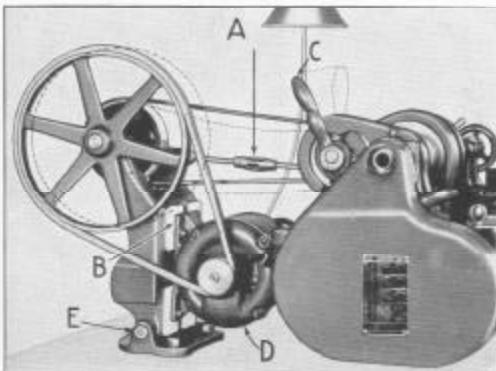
Torno de banco visto pelo extremo onde se encontra o motor horizontal ajustável.
